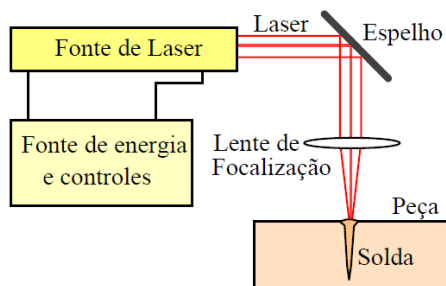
Esquematização do processo de soldadura a laser ^[52]
